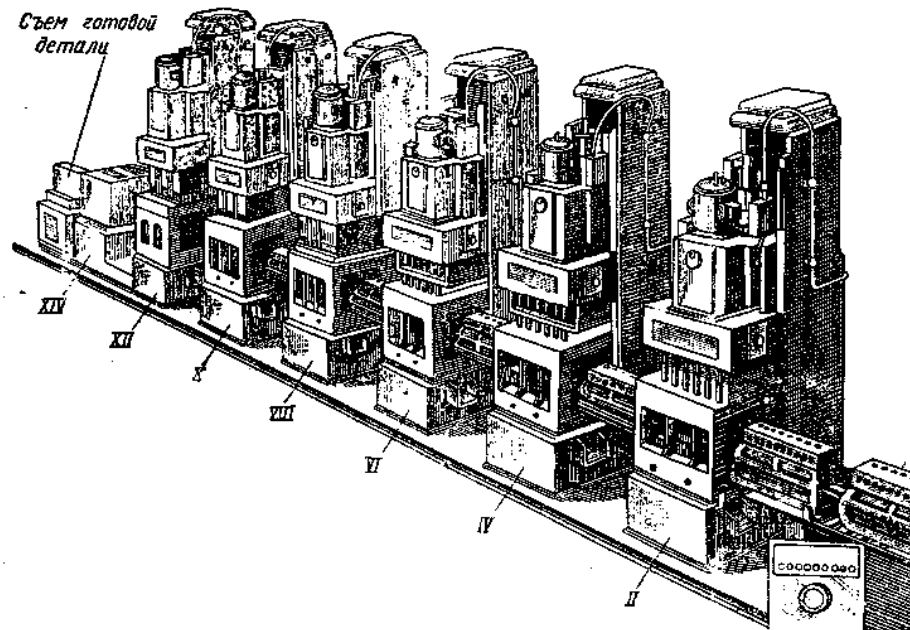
Схема компоновки автоматичної лінії із агрегатних верстатів
